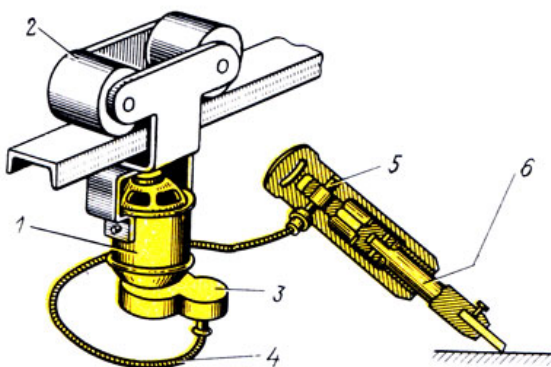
Электромеханический шабер: 1 - электродвигатель, 2 - тележка, 3 - редуктор, 4 - гибкий вал, 5 - кривошип, 6 - инструмент
